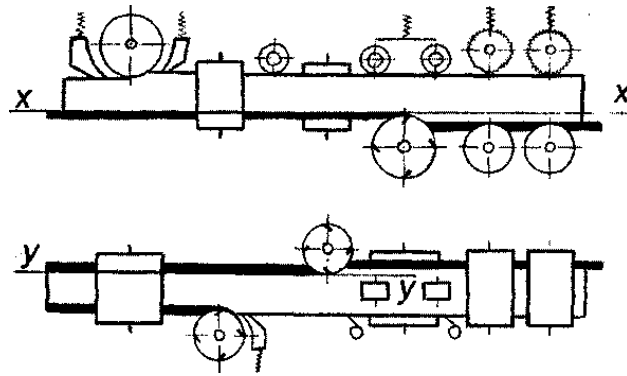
Схеми налагодження чотирибчного поздовжньо-фрезувального верстата
